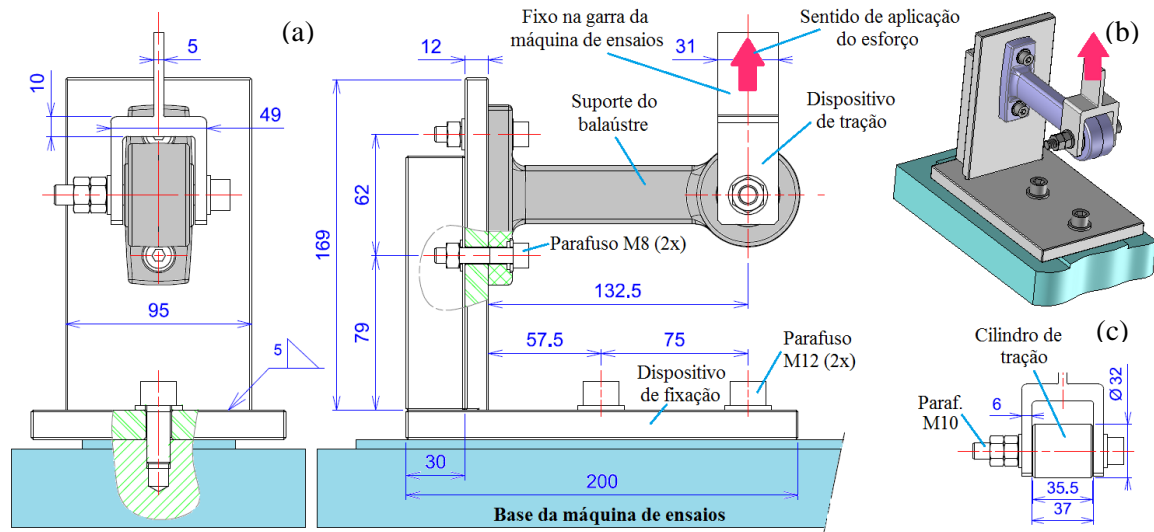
Dispositivo para fixação mecânica do suporte do balaústre. (a) dimensões. (b) vista em perspectiva. (c) detalhe do cilindro de tração
